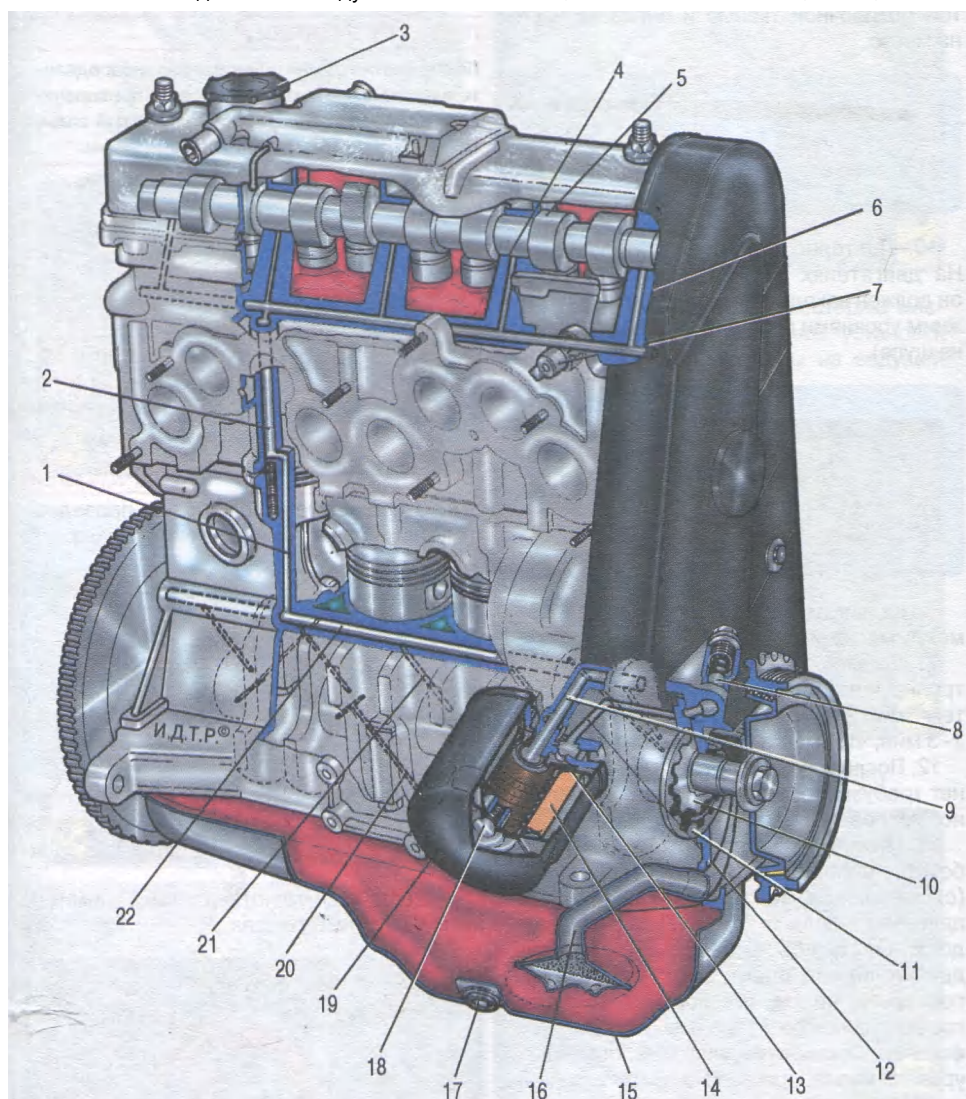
Система смазки: 1 - канал в блоке цилиндров для подачи масла в масляную магистраль головки блока цилиндров; 2 - канал в головке блока цилиндров; 3 - пробка маслоналивной горловины; 4 - масляная магистраль в головке блока цилиндров; 5 - распределительный вал; 6 - канал подачи масла к подшипнику распределительного вала; 7 - датчик сигнальной лампы аварийного падения давления масла; 8 - редукционный клапан; 9 - канал подачи масла из фильтра в главную масляную магистраль; 10 - ведущая шестерня масляного насоса; 11 - ведомая шестерня масляного насоса; 12 - канал подачи масла от насоса к фильтру; 13 - противодренажный клапан; 14 - фильтрующий элемент масляного фильтра; 15 - масляный картер; 16 - маслоприемник; 17 - пробка сливного отверстия; 18 - перепускной клапан; 19 - масляный фильтр; 20 - канал подачи масла от коренного подшипника коленчатого вала к шатунному; 21 - канал подачи масла к коренному подшипнику коленчатого вала; 22 - главная масляная магистраль
